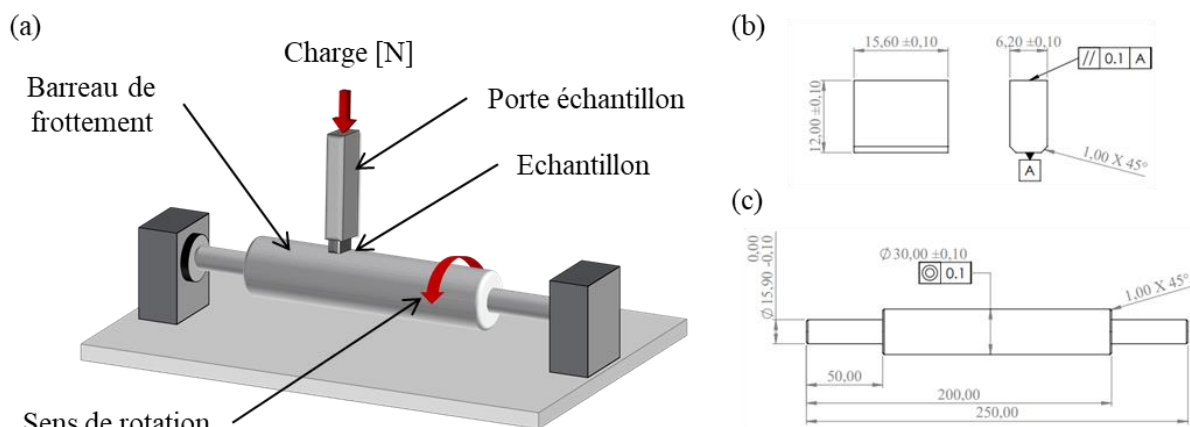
(a) Schéma de principe du test d'usure de bloc sur bague rotative, (b) dimension (mm) du bloc fabriqué par L-PBF et (c) dimension (mm) de la bague de frottement
